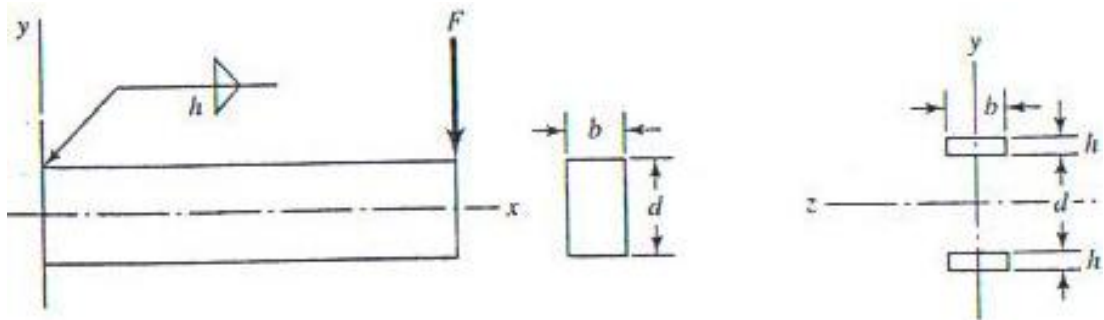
SOLDADURA DE FILETE DE VIGA SOMETIDA A FLEXION (Ref. 7)
